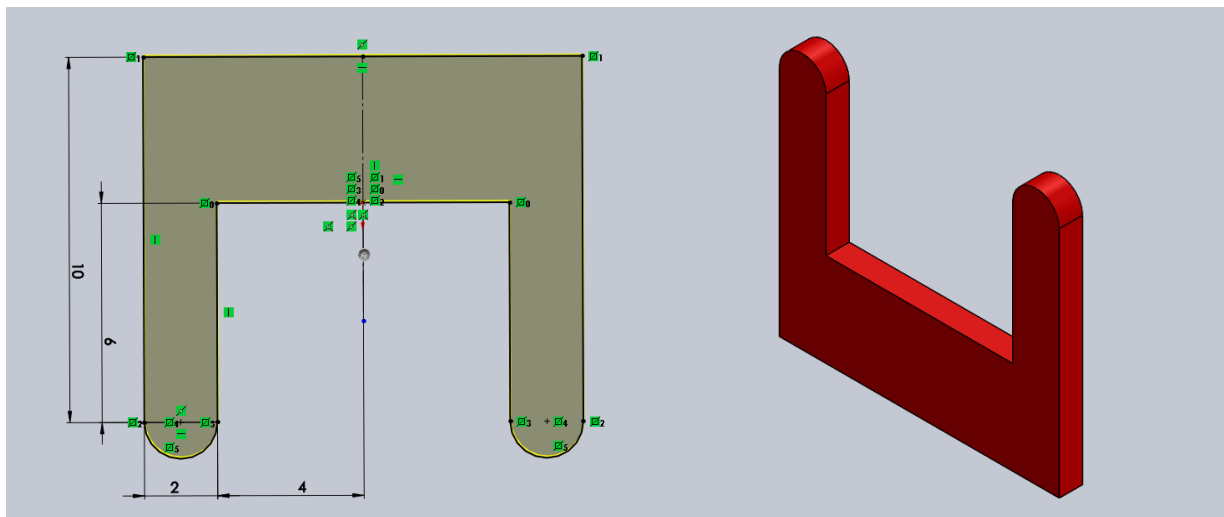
A la izquierda: extrusión desde su croquis a una cota de 1mm. A la derecha: perspectiva de la pieza terminada.
